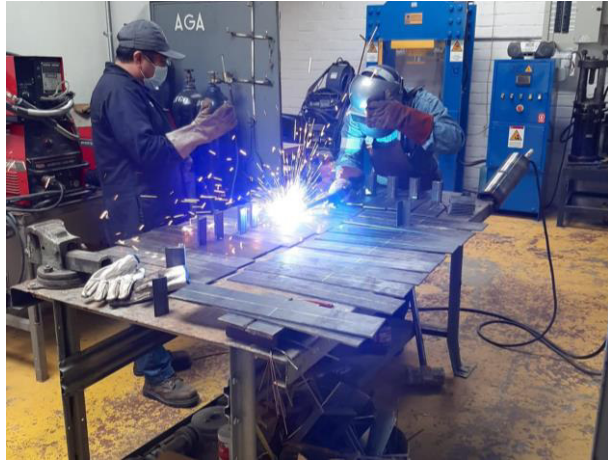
Proceso de soldadura de conectores de corte al patín de la viga
